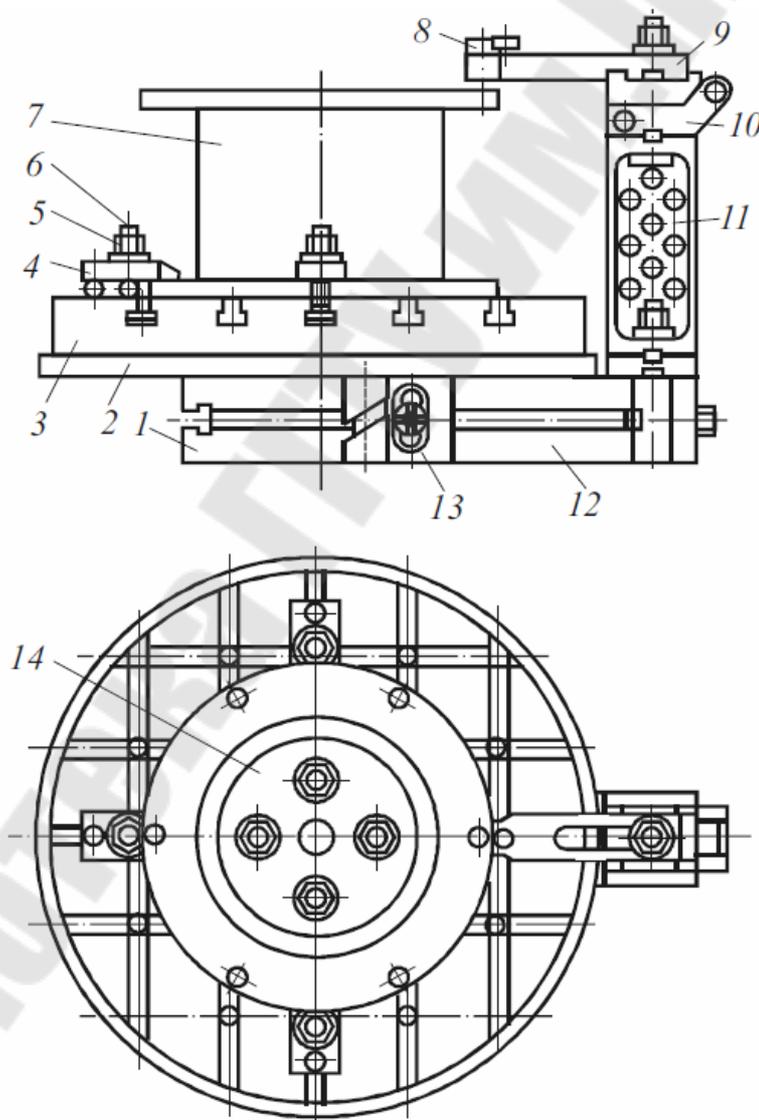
Универсально-сборное приспособление для шлифования рабочих поверхностей призм [4]
